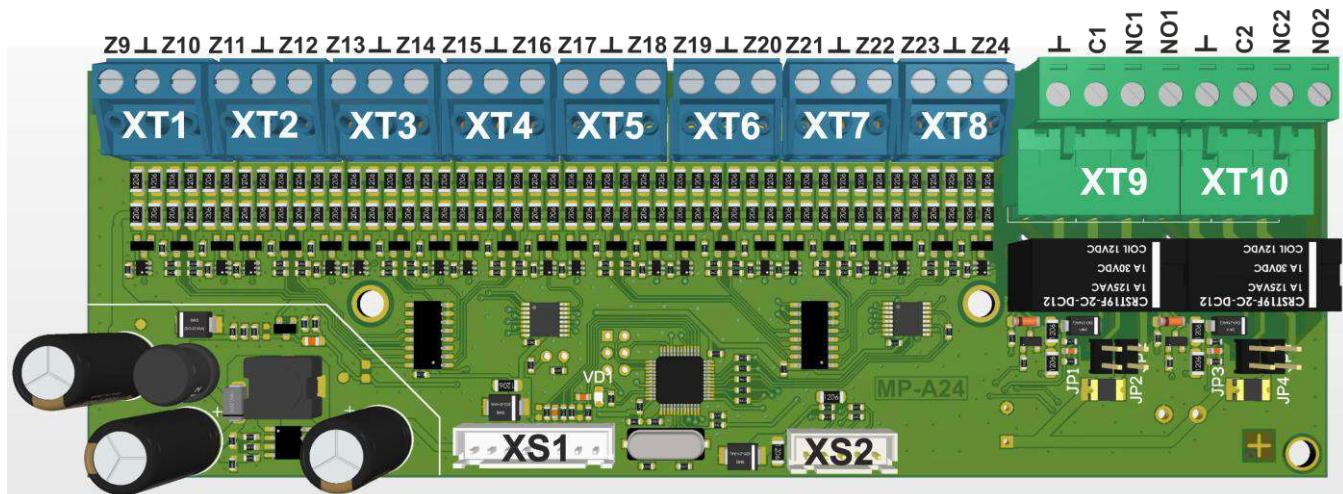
Внешний вид и обозначение элементов MP-A24/16
